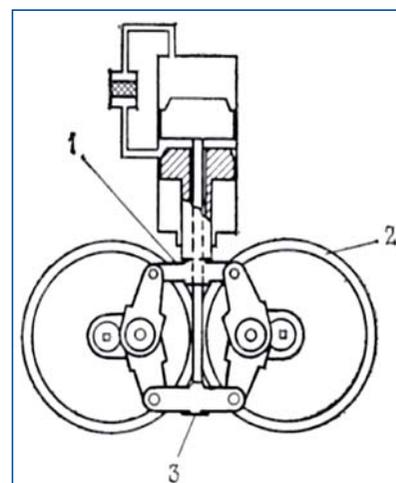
"Ромбический привод" двигателя Стирлинга:
